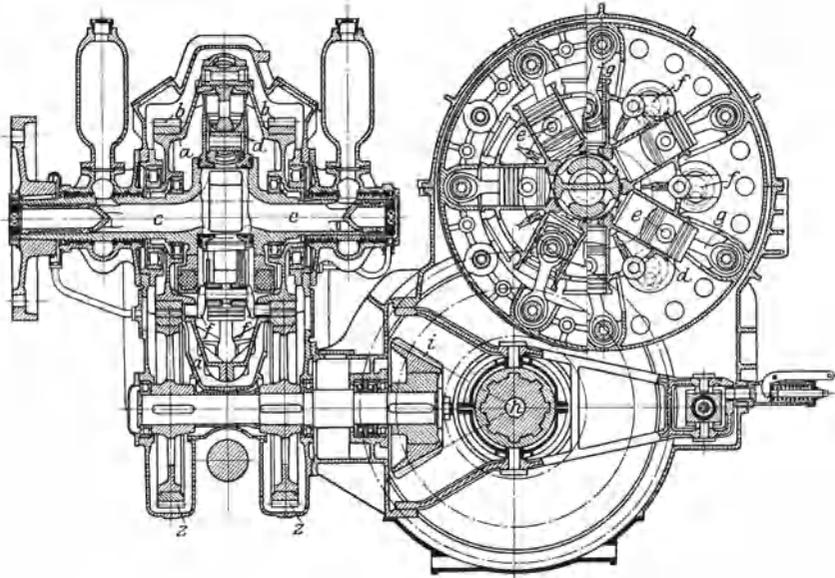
Schneider-Kolben-Getriebe. Längsschnitt durch das Primärgetriebe. Querschnitt durch das Sekundärgetriebe. (Schweiz. Bauzg. 1925, S. 125.)
